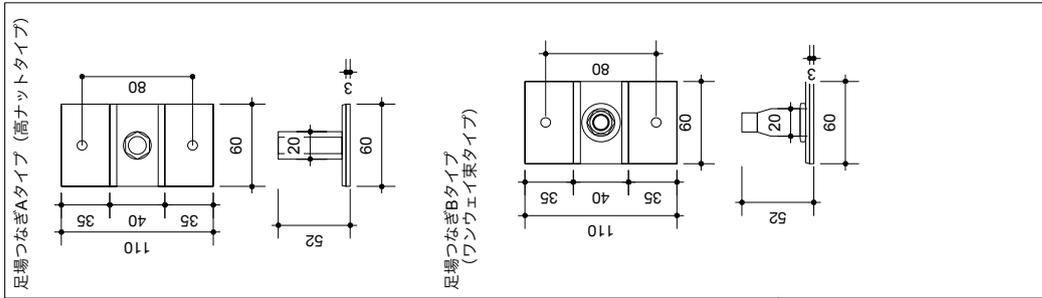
試験体 1 の構造・寸法 (単位 : mm)
